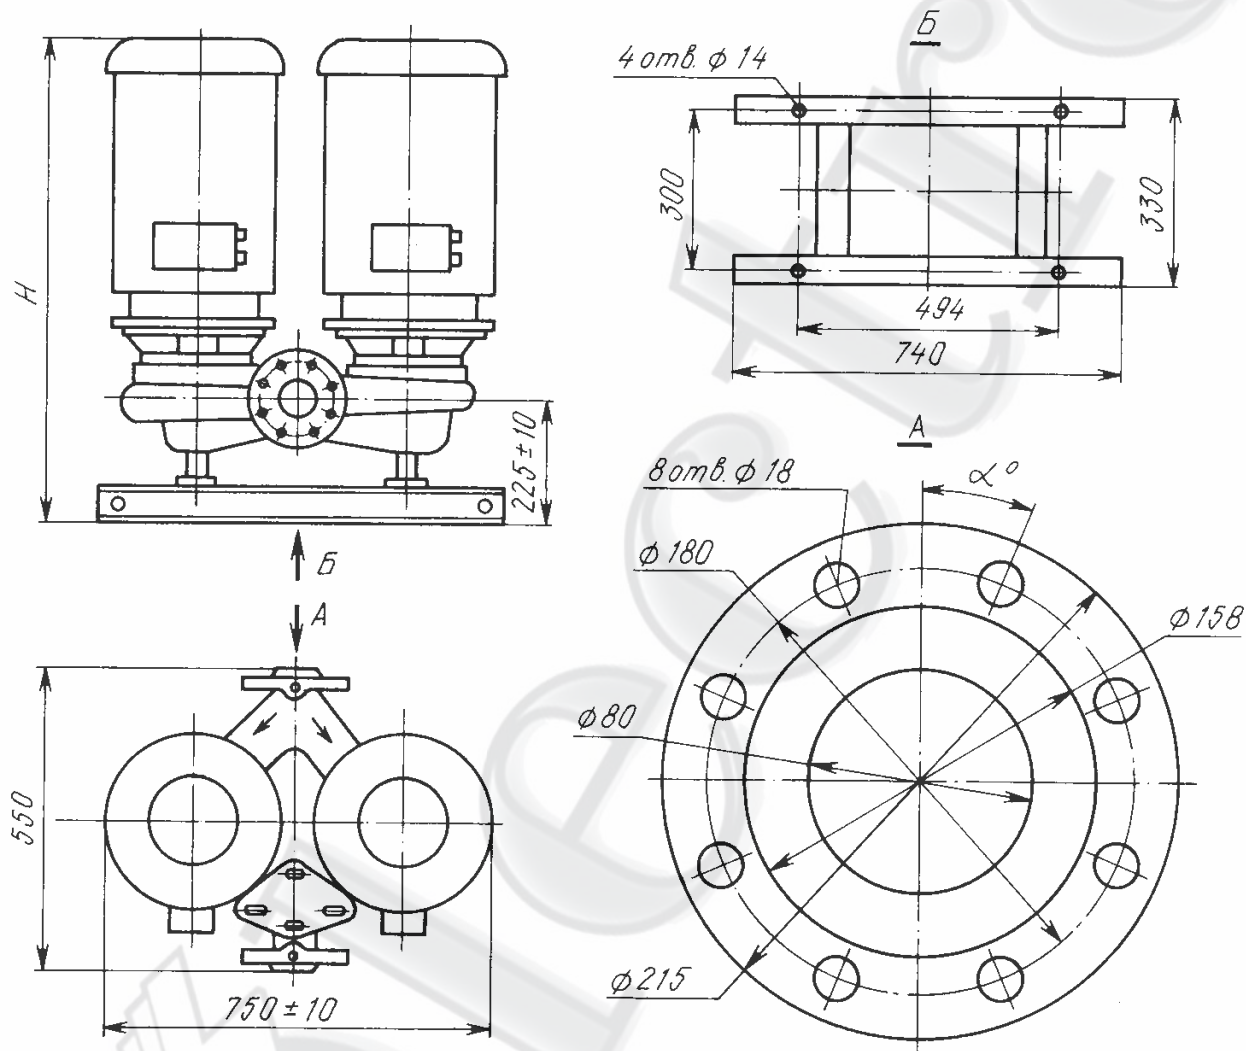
Общий вид, габаритные, установочные размеры и масса электронасосов KMC80-200/2
